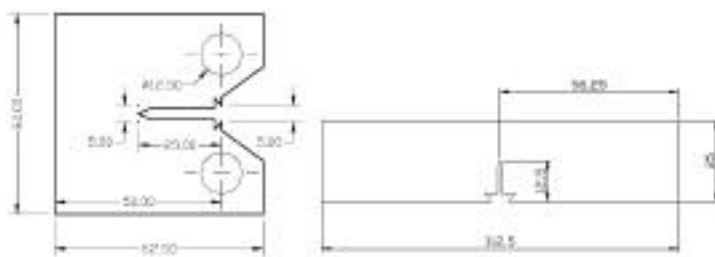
Dimensões dos corpos de prova C(T), ($W = 50,0$ mm) e SE(B), ($W = 25$ mm).
